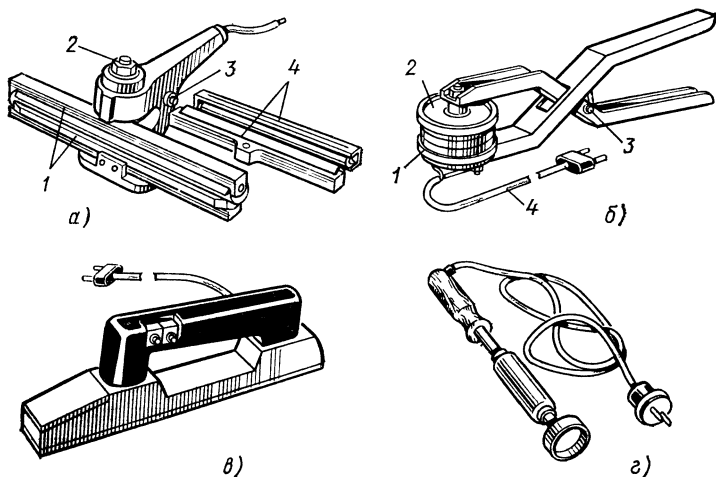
Устройства и приспособления для сваривания полимерных материалов:
